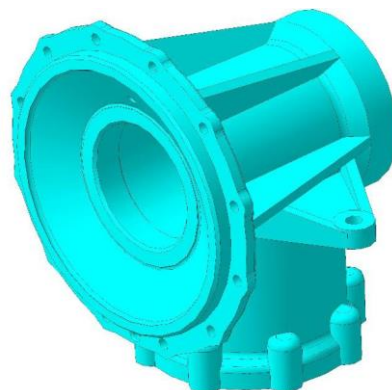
Тривимірна модель корпусу планетарно-конічного редуктора
